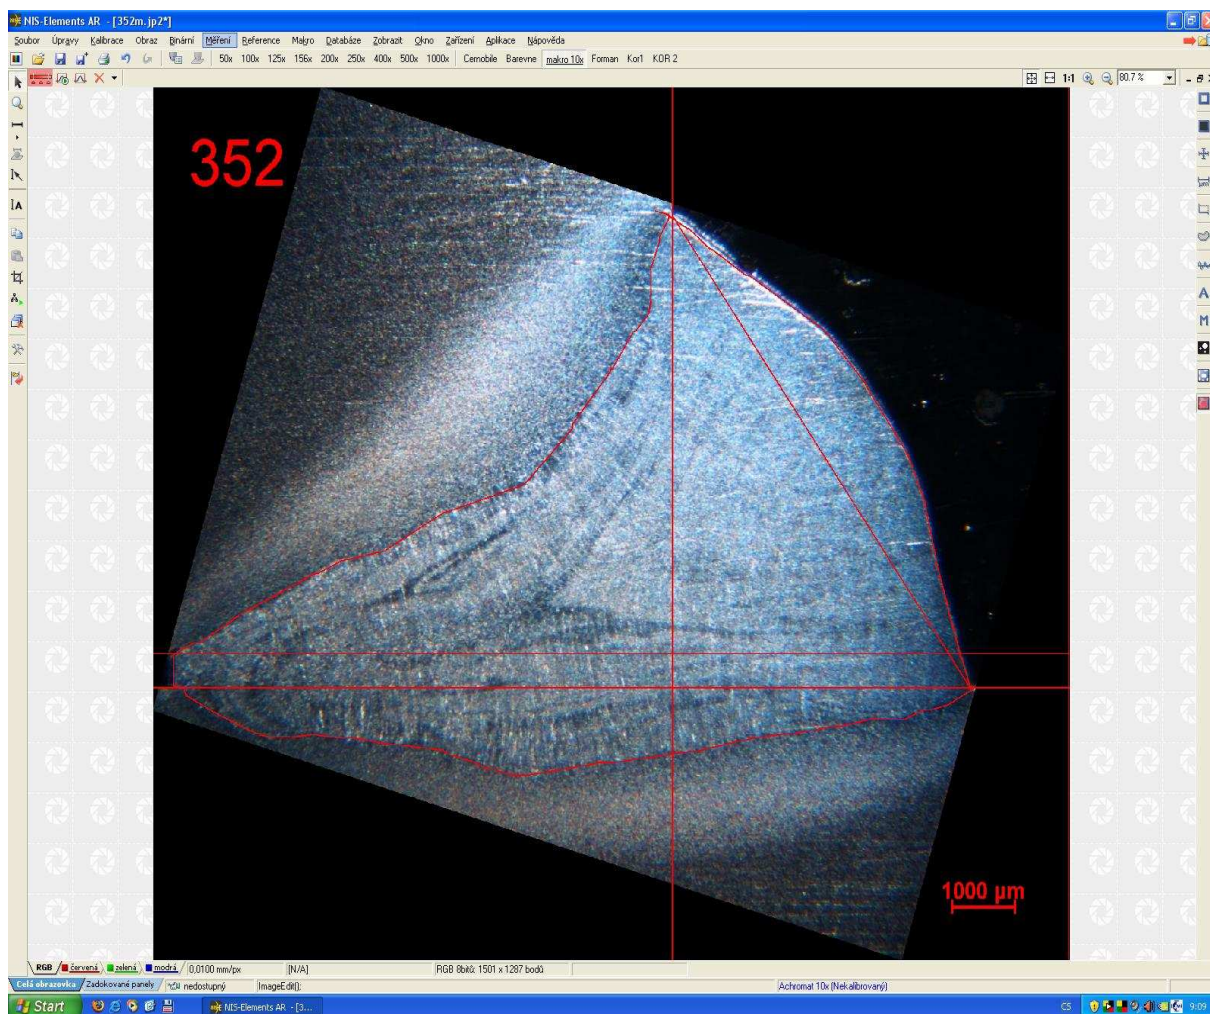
Laboratoř pro vyhodnocování makrosnímku
